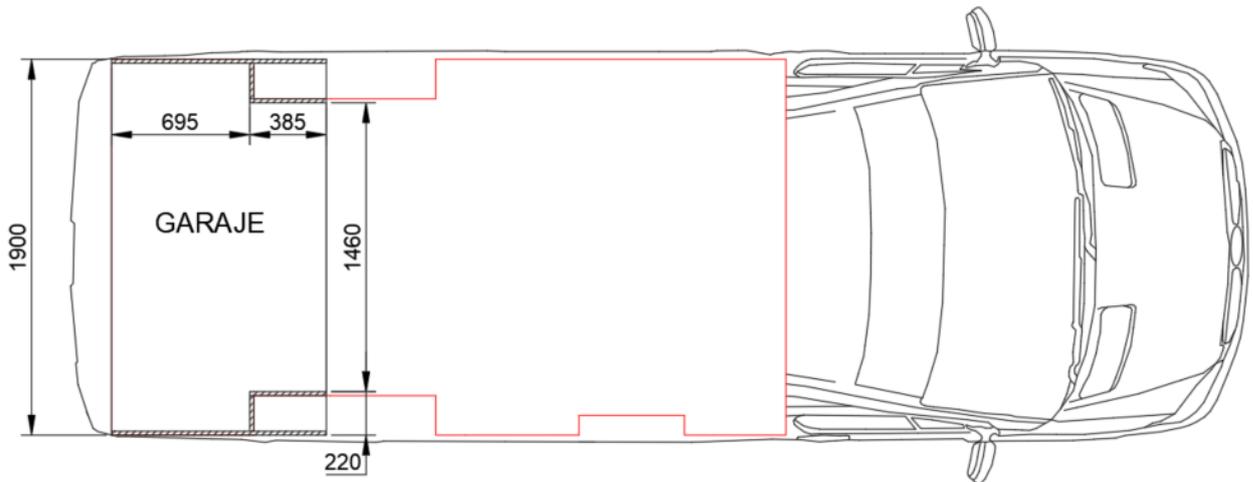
Disposición módulo garaje. Fuente: Elaboración propia
